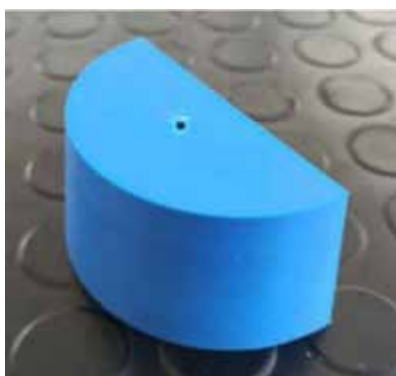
Результат виготовлення деталі "Платформа камери"
